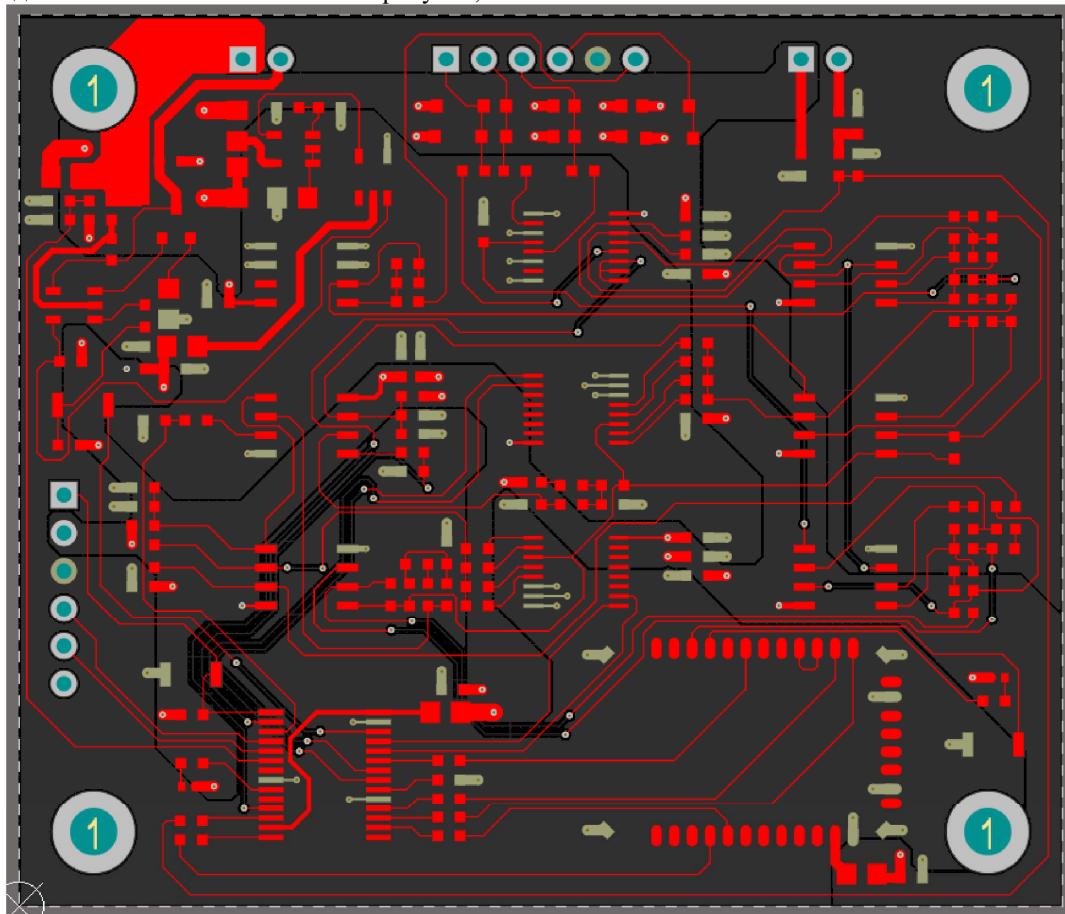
Печатный рисунок на верхнем слое двухслойной печатной платы с полигонами
